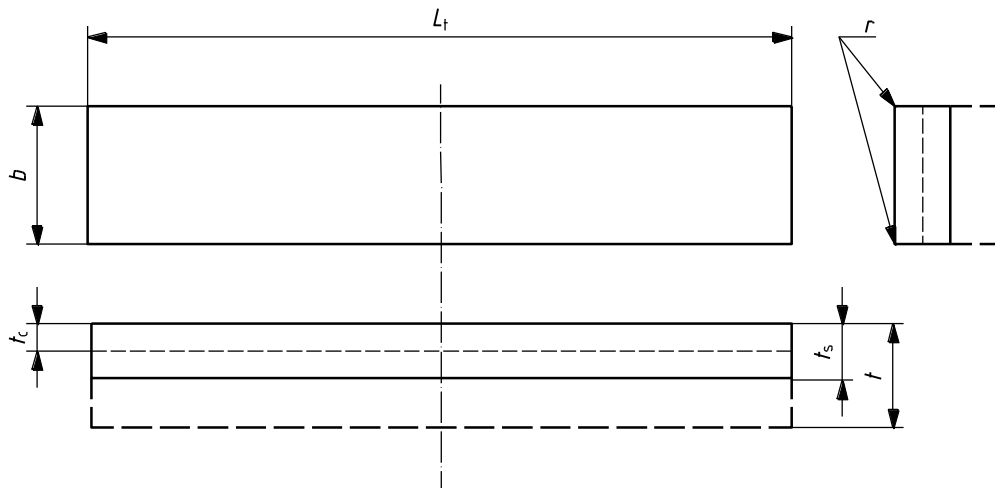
Образец для испытаний на загиб с растяжением лицевой стороны для плакировки без стыкового сварного шва (FBC)
